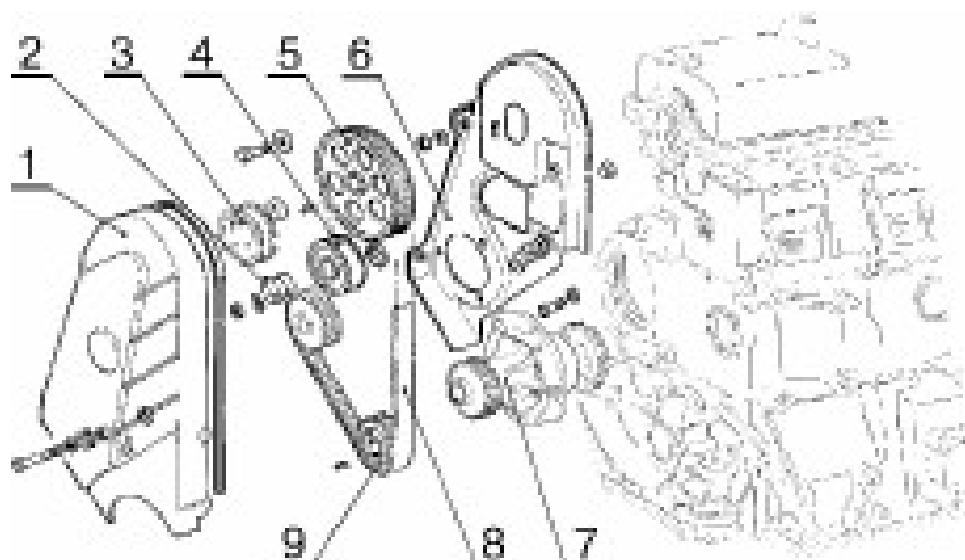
Схема демонтажу деталей приводу газорозподільчого механізму
